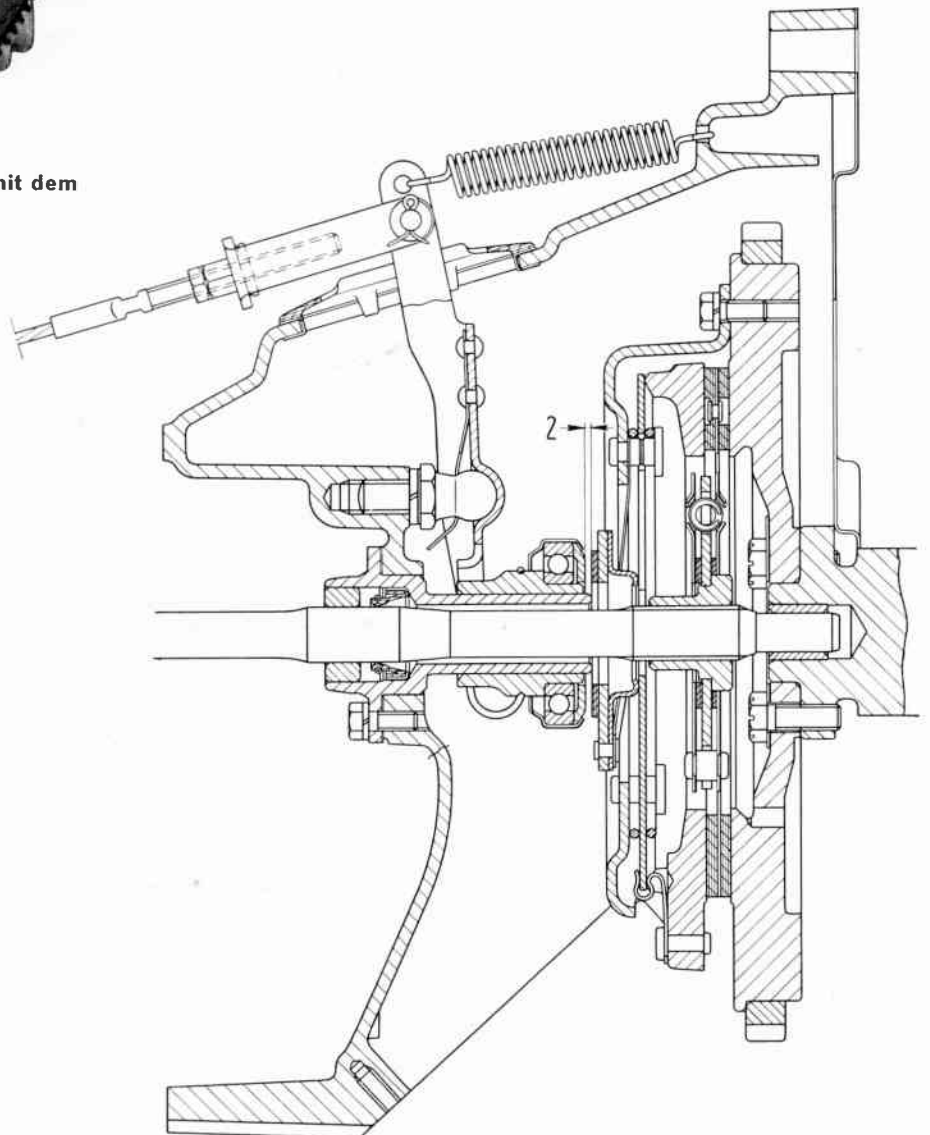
Längsschnitt der Kupplung und ihrer Ausrückvorrichtung.
